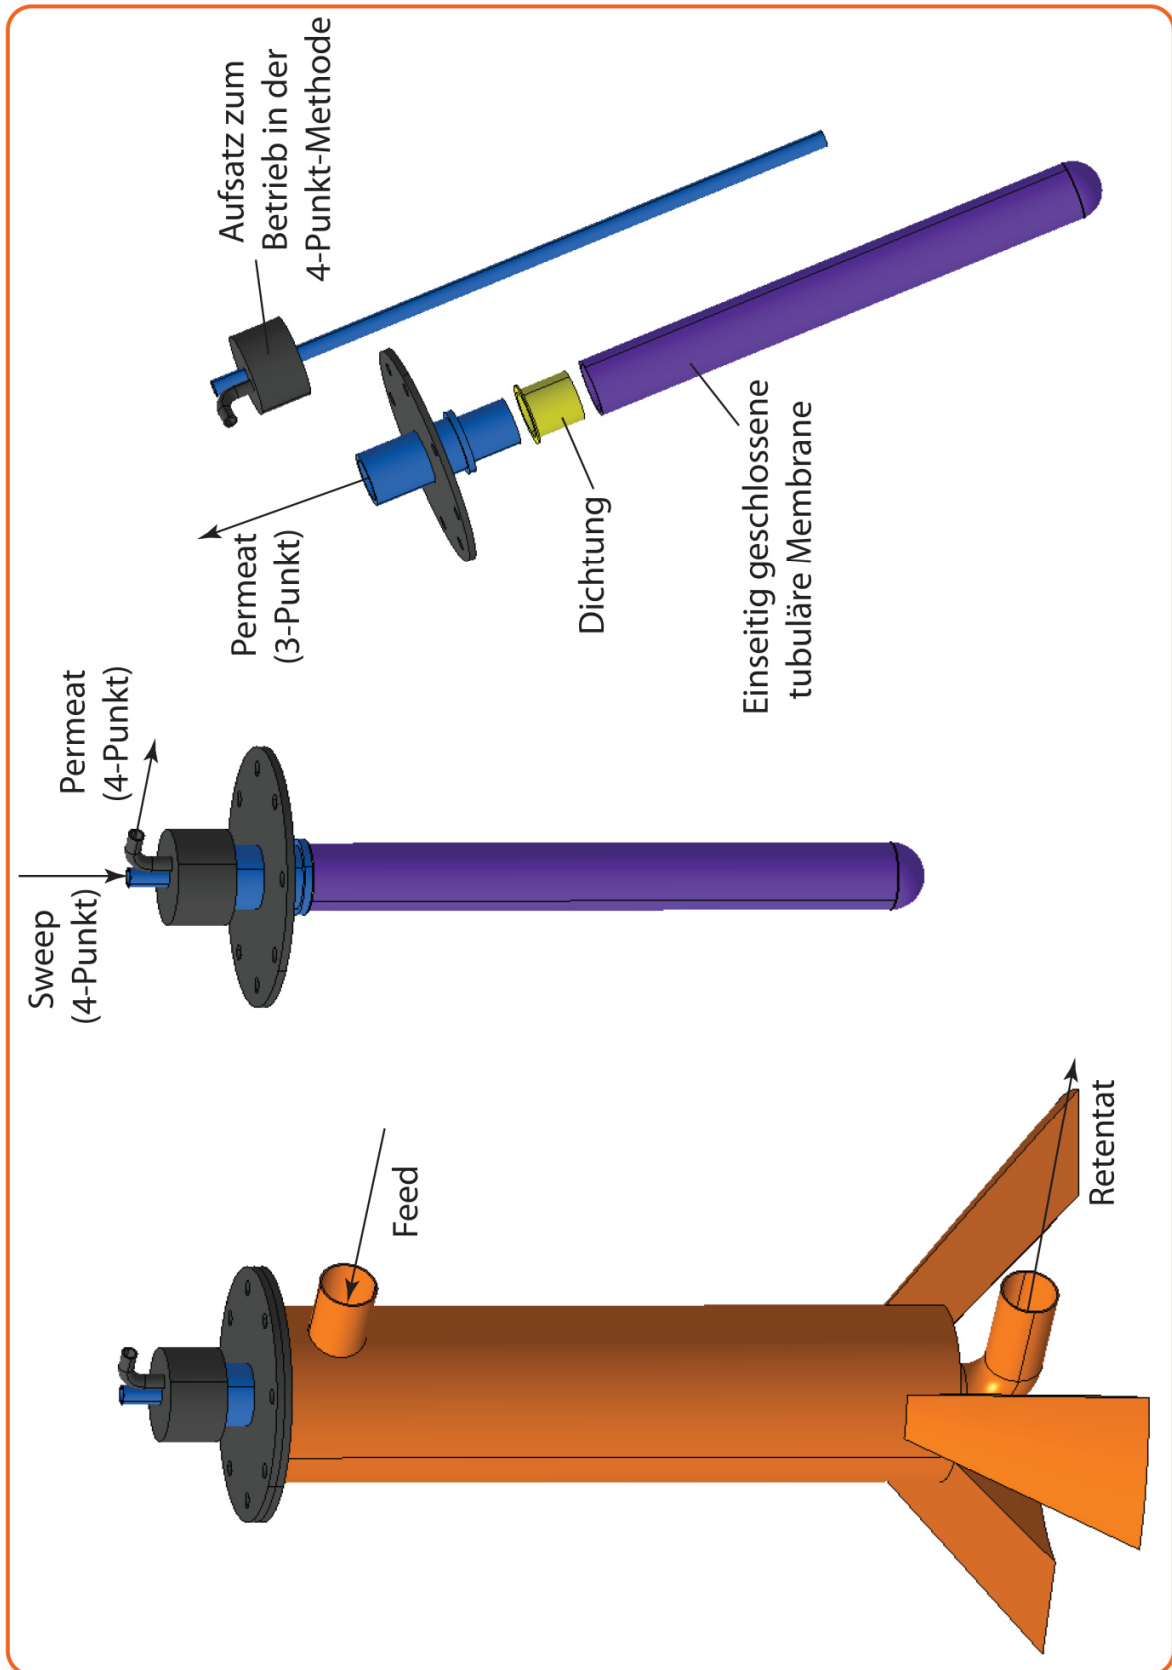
Gehäuse für einseitig geschlossene, tubuläre Membranen
